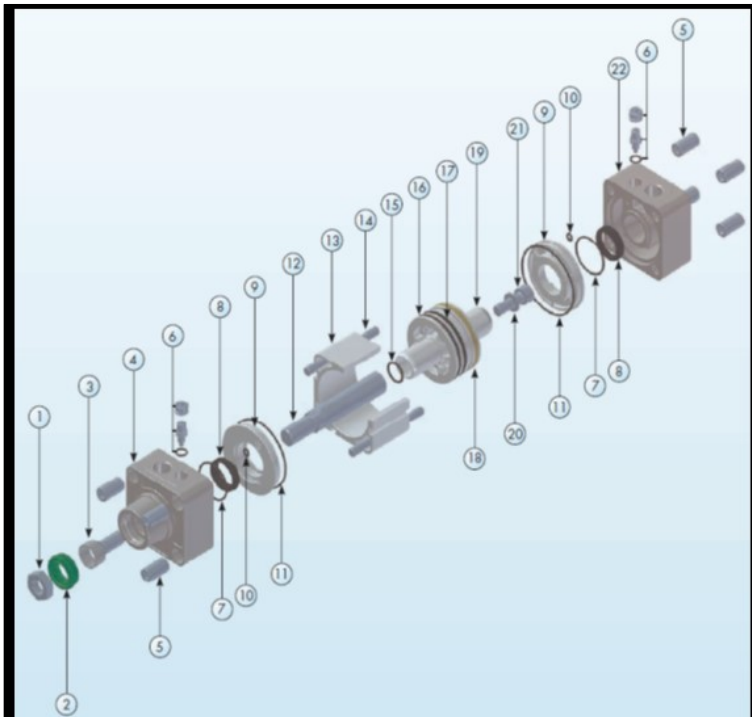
Explosionsdarstellung Pneumatikzylinder (Kuhnke, 2018)
